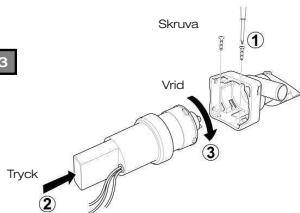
Pumpen skall inte skruvas direkt på skrovet
